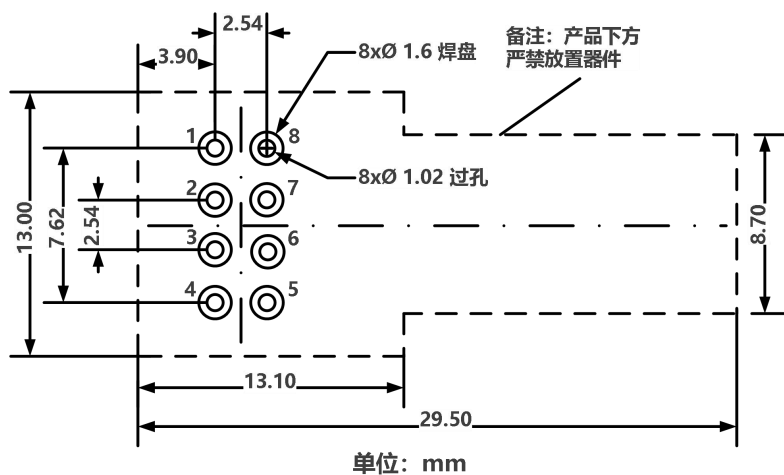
PCB Layout 设计推荐尺寸图 (俯视图)
